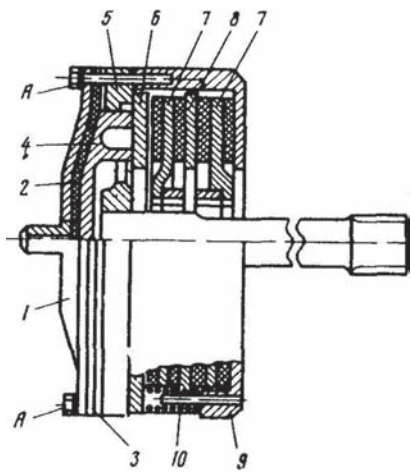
Муфта АБД. 1 — крышка диафрагмы, 2 — диафрагма, 3 — прокладка, 4 — нажимной диск, 5 — блокировочный вал, 6 — отжимной диск, 7 — соединительный диск с накладками в сборе, 8 — промежуточный диск, 9 — корпус со штифтами в сборе, 10 — пружины фиксатора, А — болты
